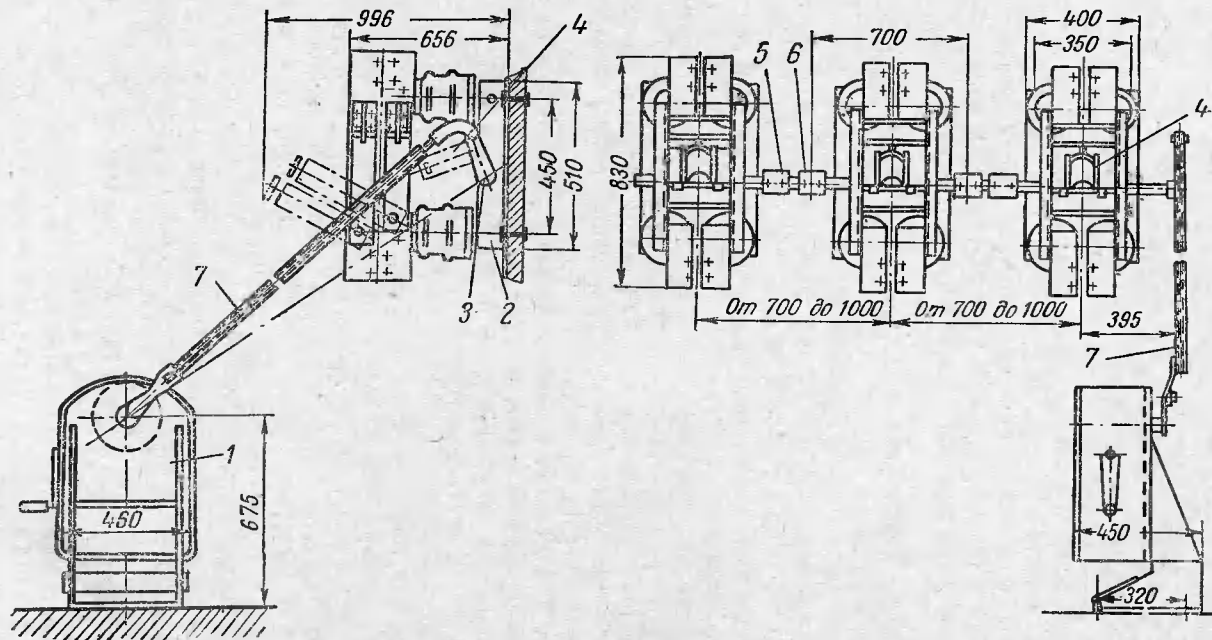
Установка трехполюсного разъединителя типа РВК с моторным приводом типа МГВ.
